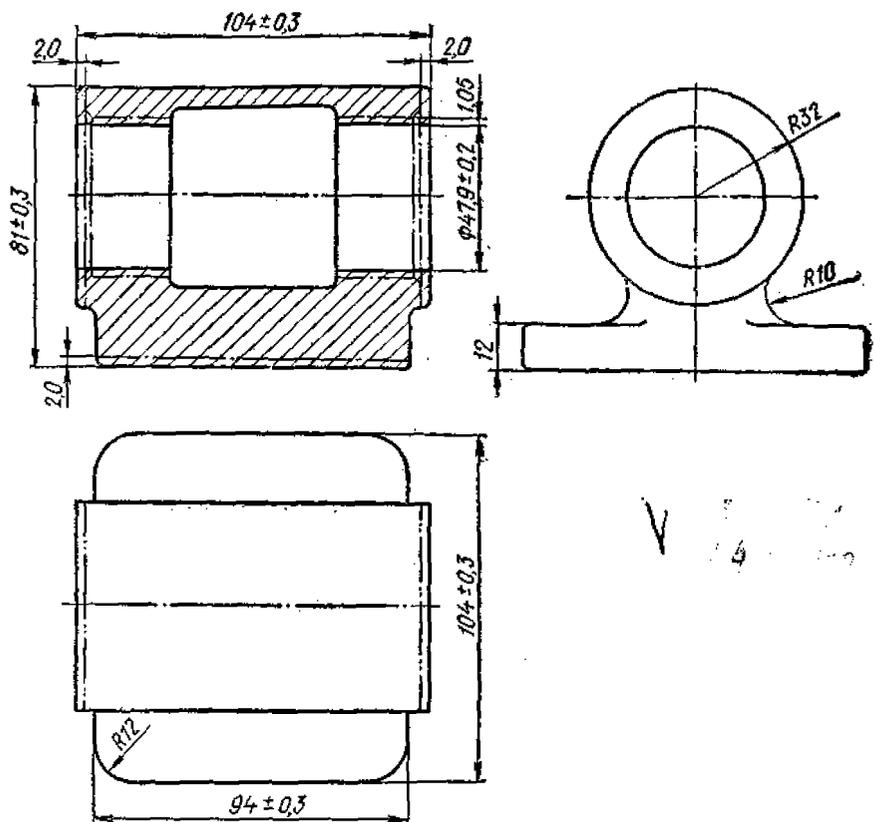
Заготовка корпуса (рис. 15) с начисленными припусками и допусками
